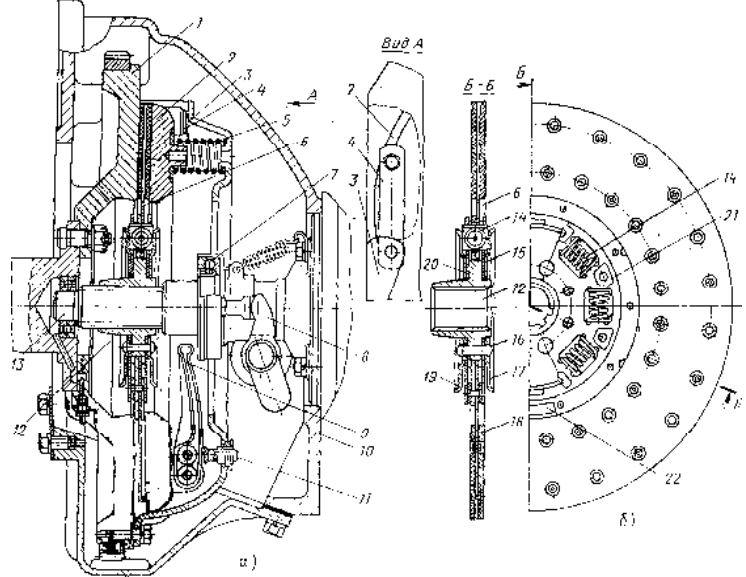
Сцепление автомобиля ЗИЛ-130: а – общий вид; б – ведомый диск.
